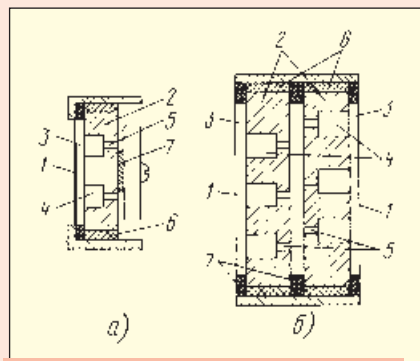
а — одномембранный микрофон; б — двухмембранный микрофон; 1 — мембрана; 2 — неподвижный электрод; 3 — воздушный зазор; 4—5 — отверстия акустических каналов; 6 — изолирующее кольцо; 7 — калиброванные прокладки
